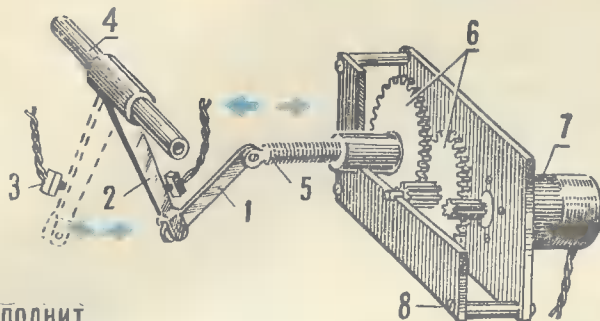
Механизм выпуска щитков: 1 — промежуточное звено; 2 — качалка; 3 — концевые выключатели; 4 — вал для выпуска и уборки щитков; 5 — винт М4; 6 — зубчатое колесо; 7 — электродвигатель; 8 — стойка.
